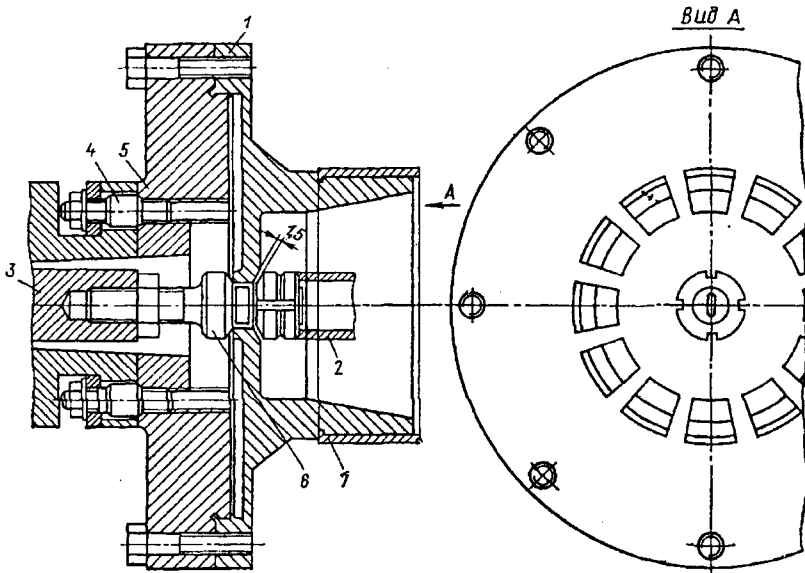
Мембранний патрон для обробки вкладишів шатуна опозитного компресора бази М10.
